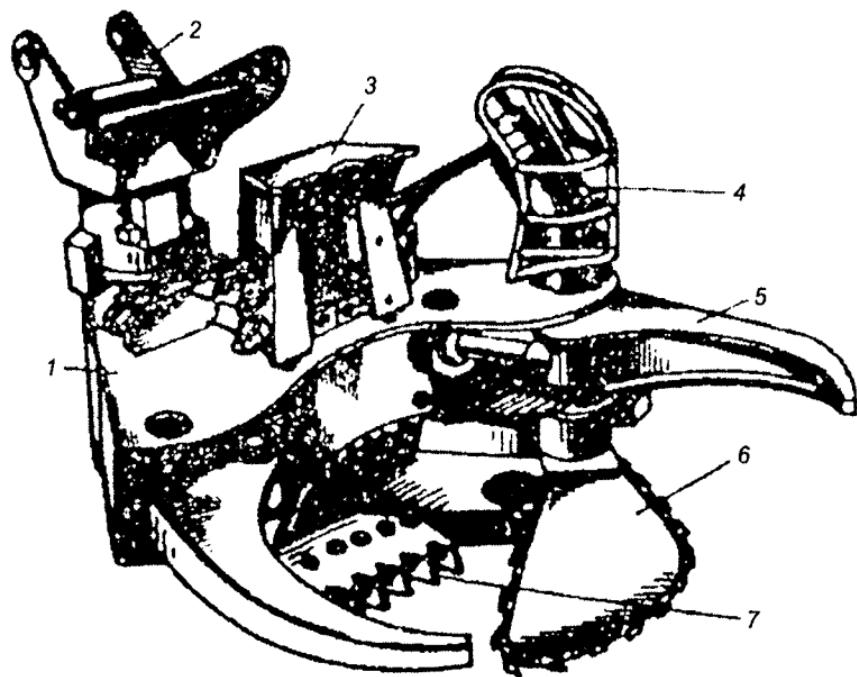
Захватно-срезающее устройство ВТМ ЛП-17, ЛП-17А
